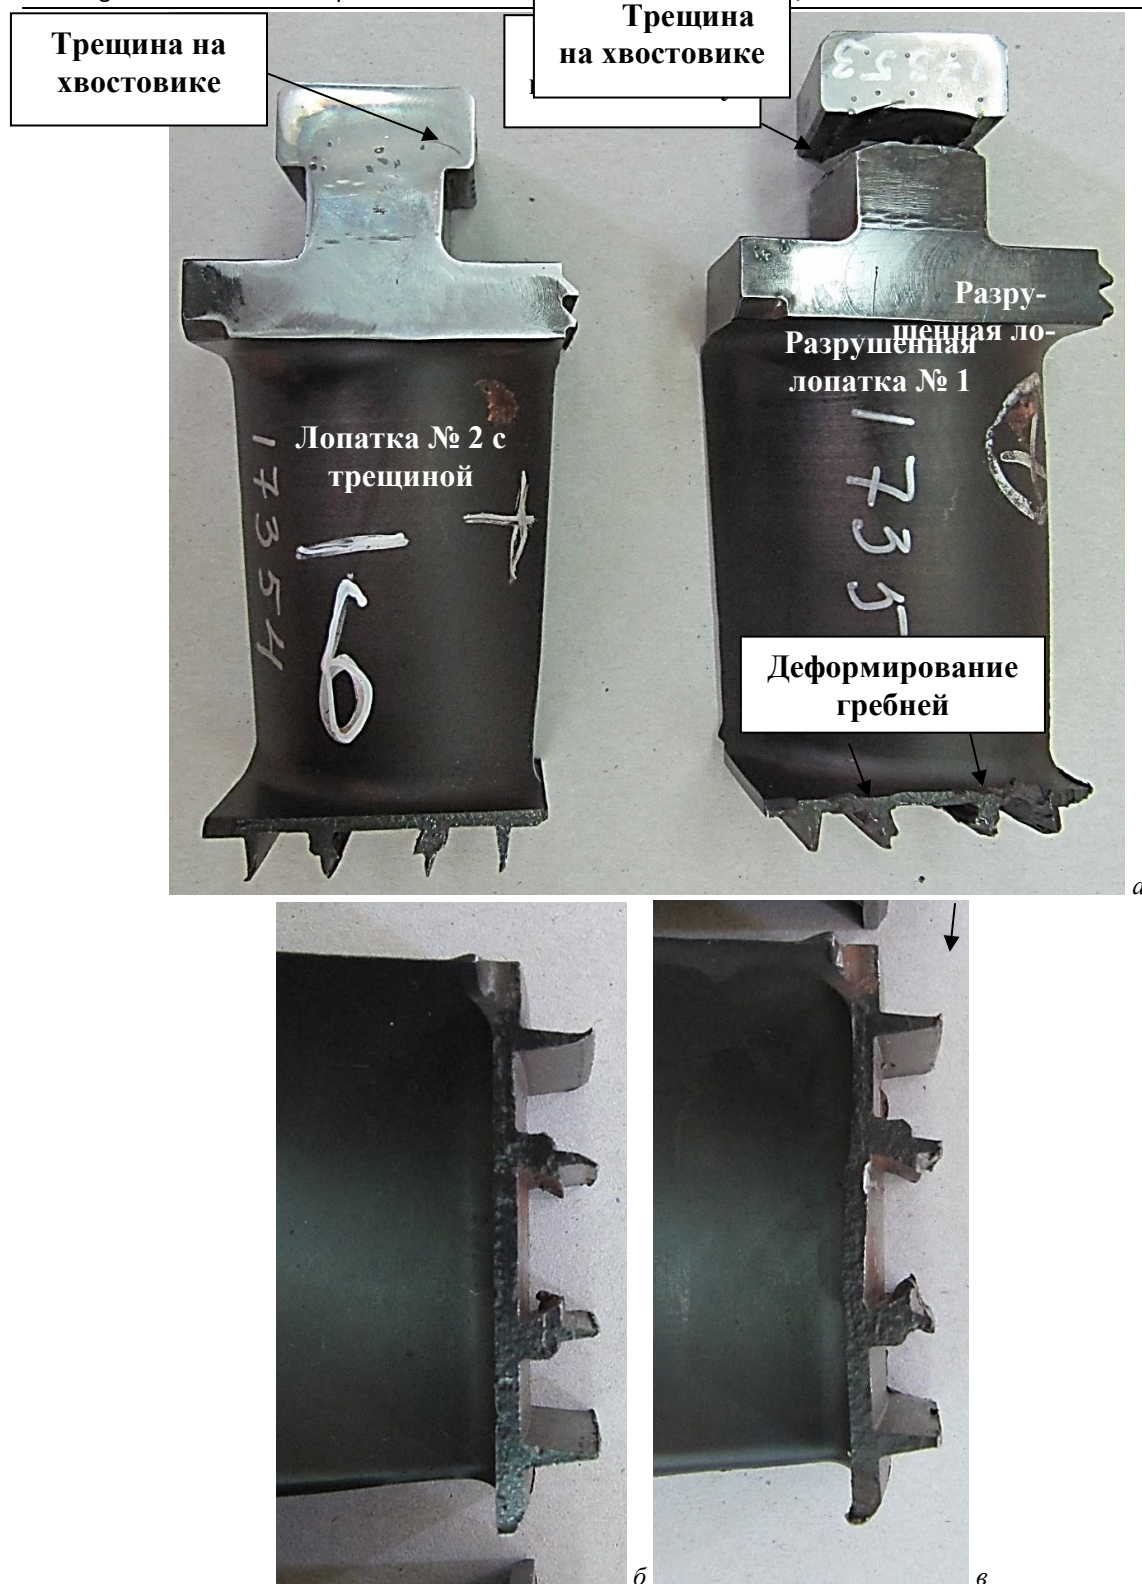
Общий вид лопаток: а – лопатка с трещиной и разрушенная лопатка; б, в – смятые и погнутые радиальные уплотнительные гребни
